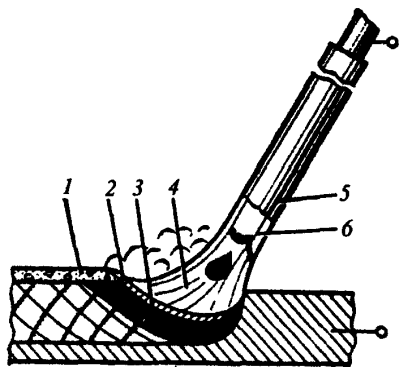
Схема дуговой электрической сварки металлическим электродом:
